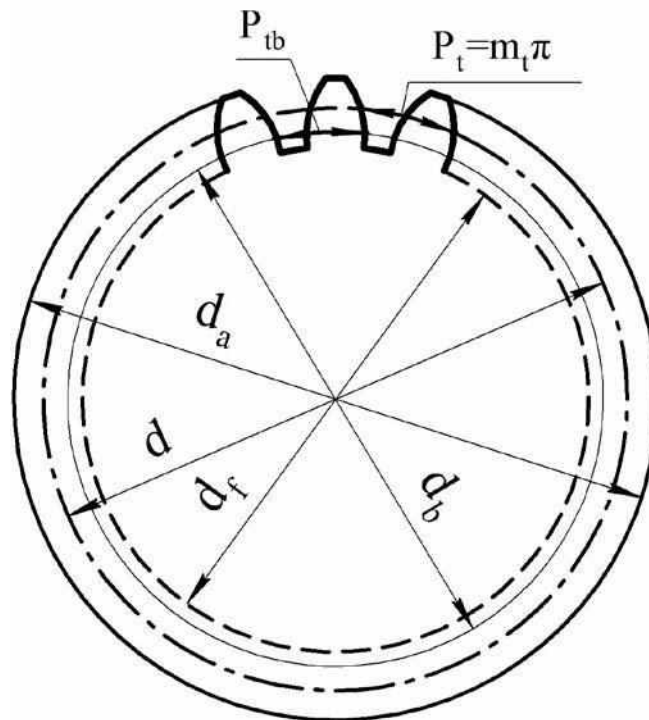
Эвольвентное цилиндрическое колесо: диаметры и шаги зацепления
